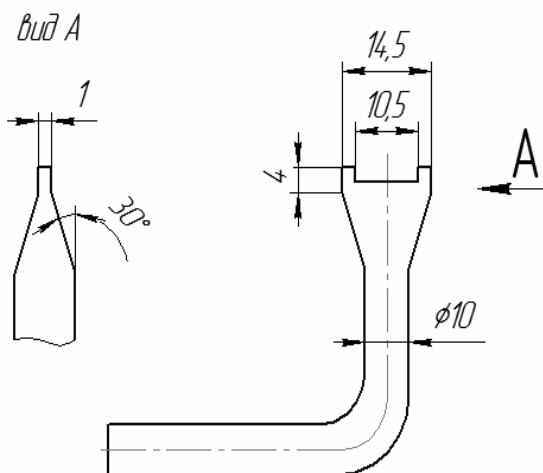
Специальная отвертка для разборки и сборки клапанов бустера.
